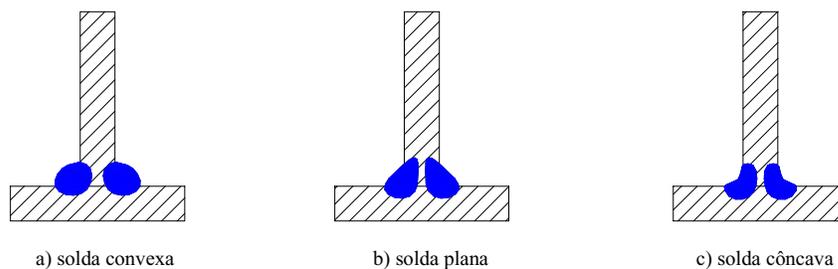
Tipos de cordões de solda – SOUZA^{67, 68}
